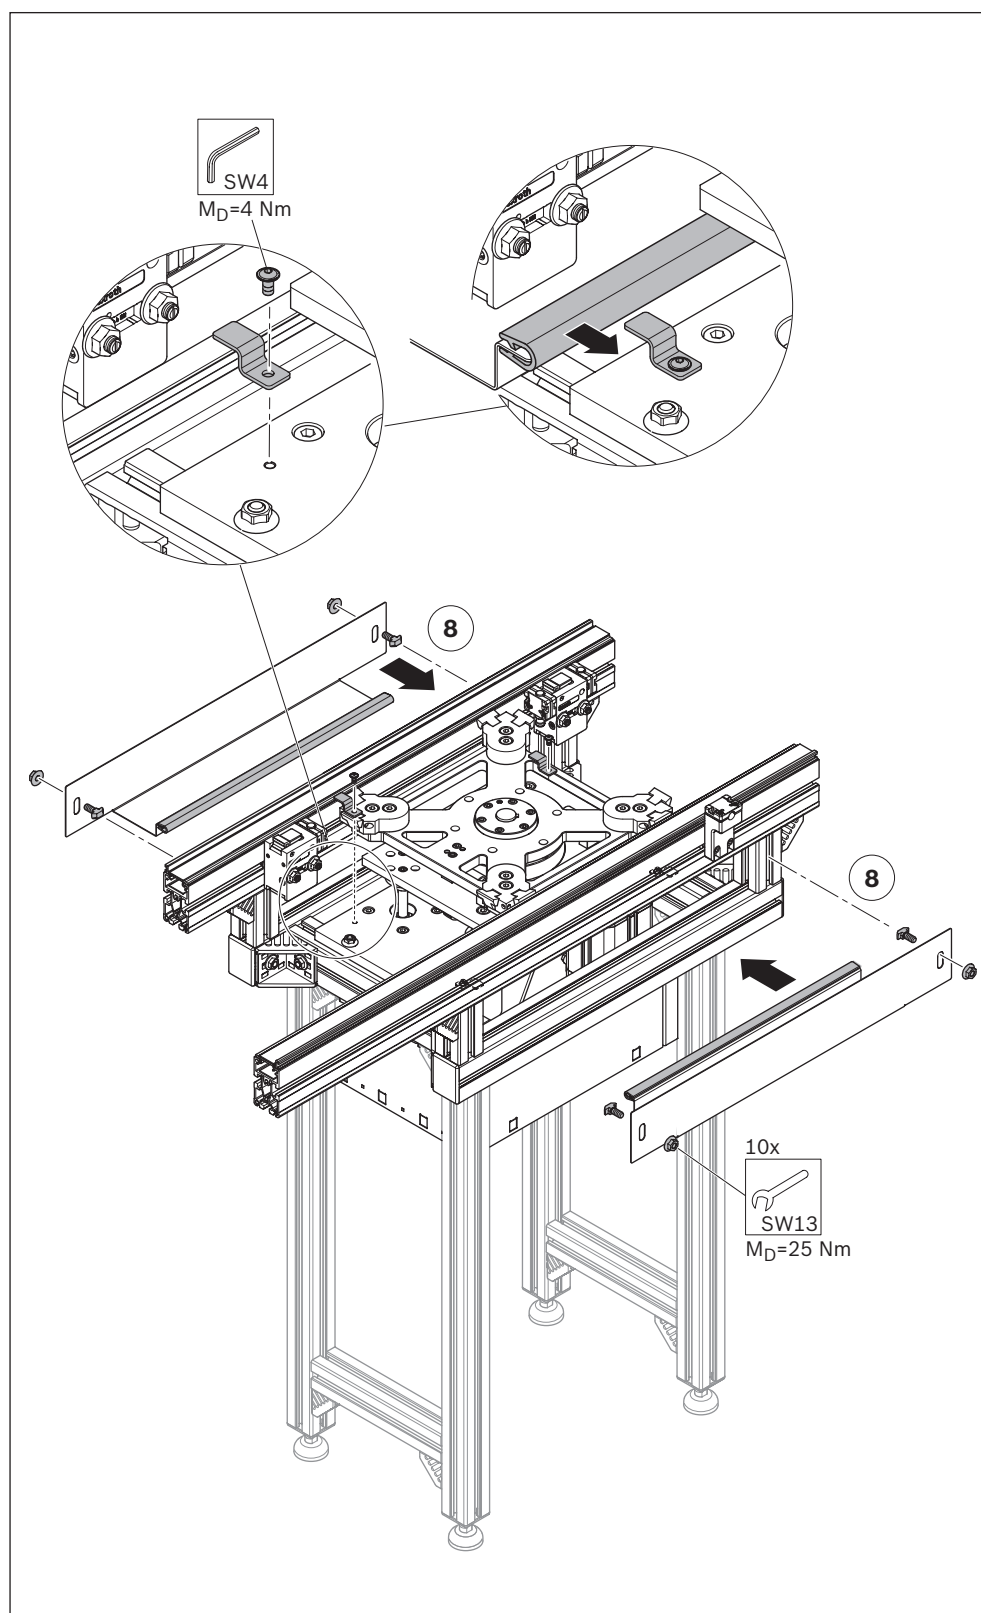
Montaje de las chapas de protección frontales (aquí tamaño constructivo 2 180° para WT 2, WT 2/F)
